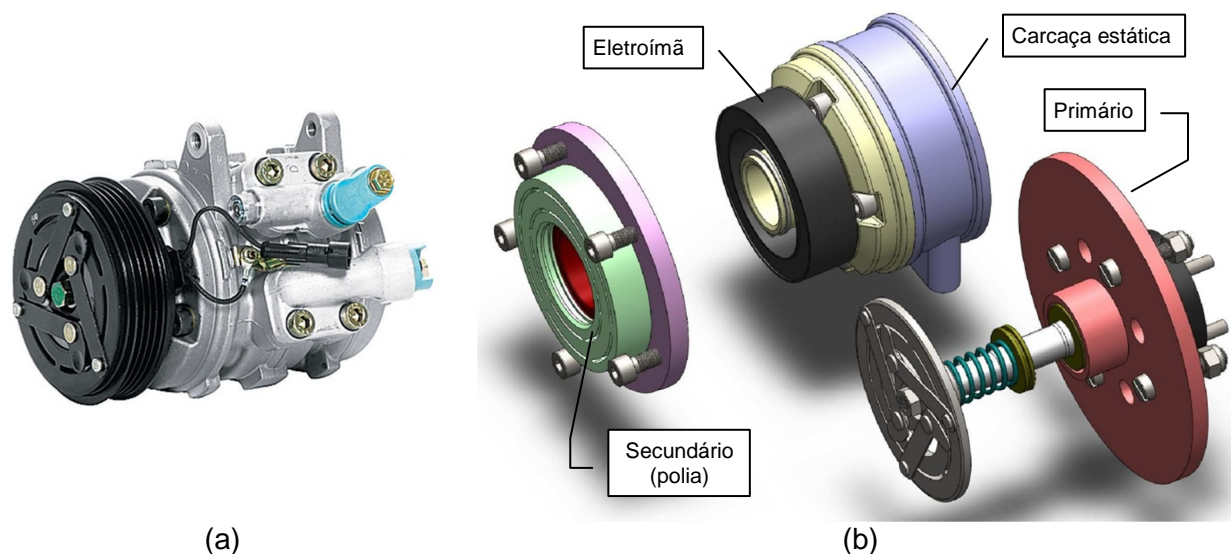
Compressor: (a) Original; (b) Adaptado para receber os volantes (vista explodida)
